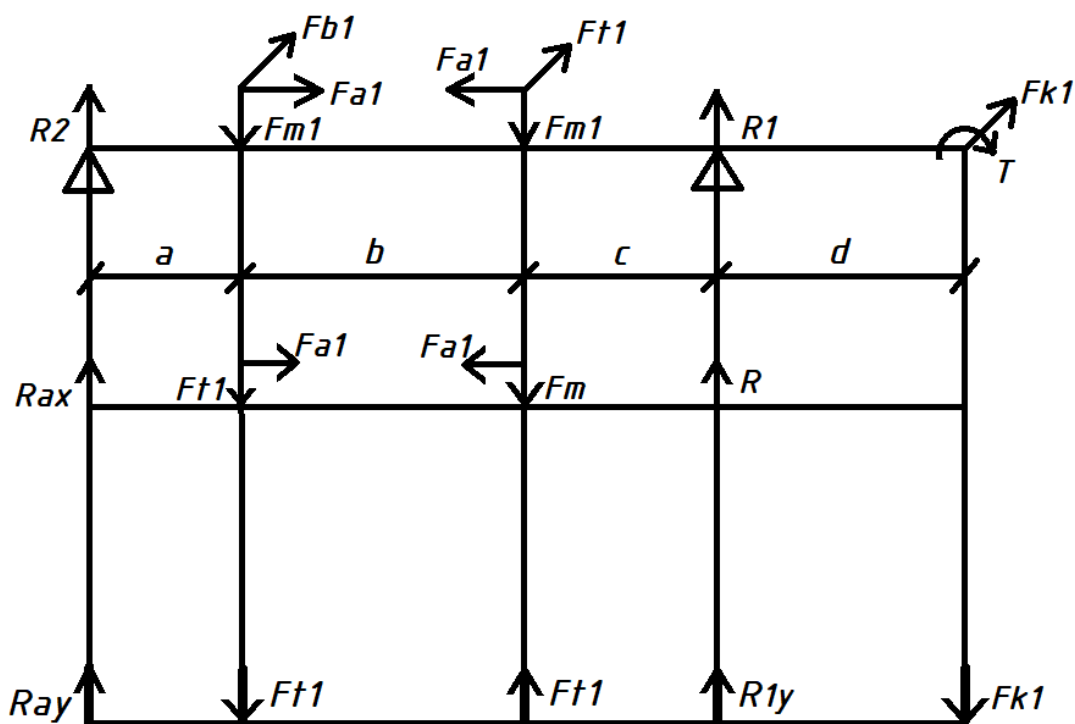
Розрахунква схема для вала-шестерні
